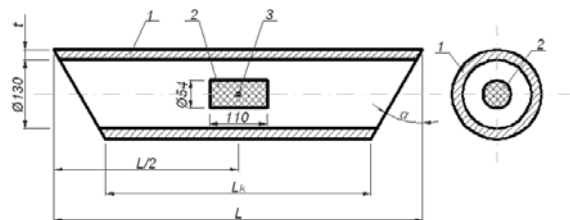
Схема корпусу контейнера для знешкодження СВП:
